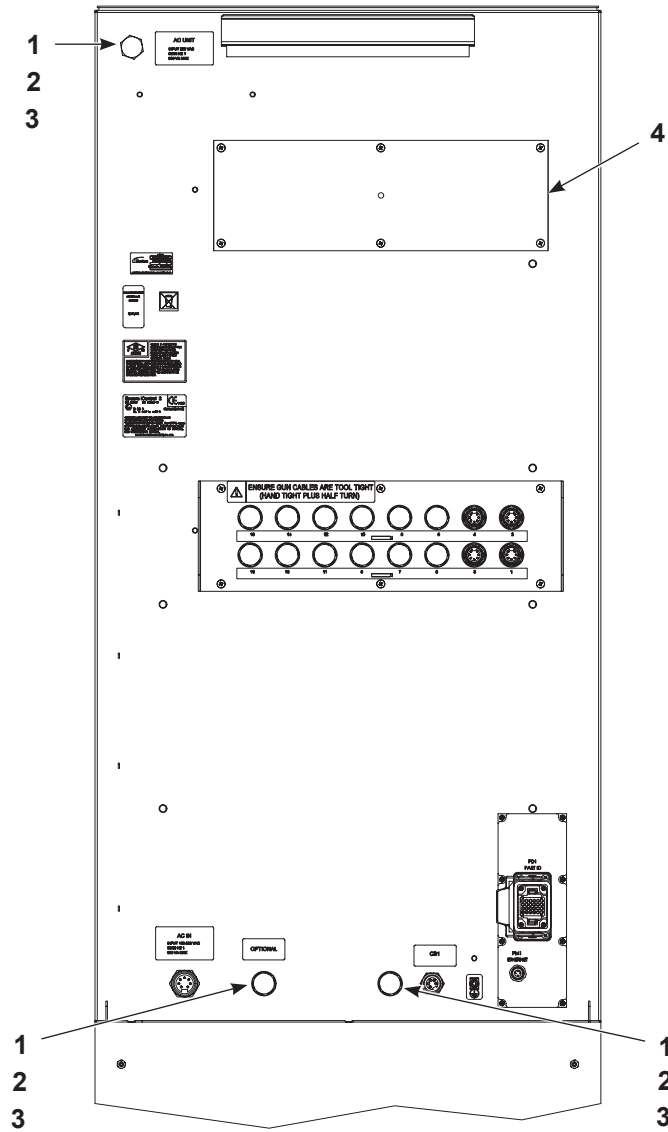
Pièces de la console principale et auxiliaire – Vue arrière (1 sur 3)
